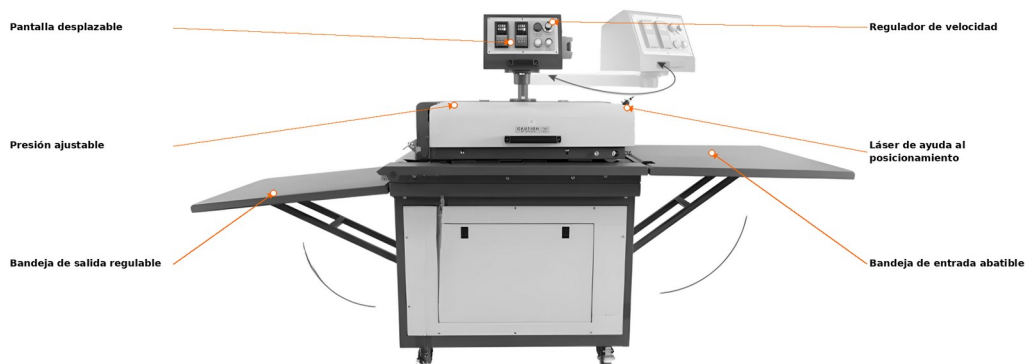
· Componenti principali della macchina Beinsen Tobago.
